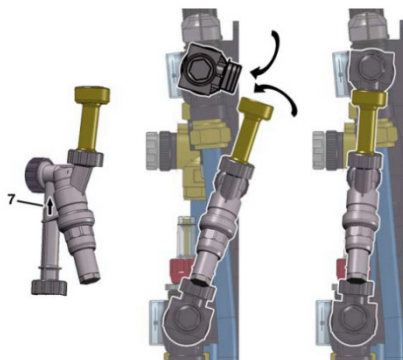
Montaż elementu przedłużającego 35 mm
